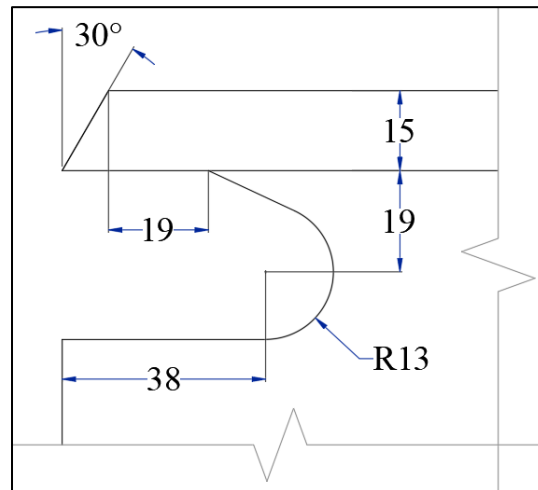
Esquema de agujero para soldadura (elaborado por el autor)
